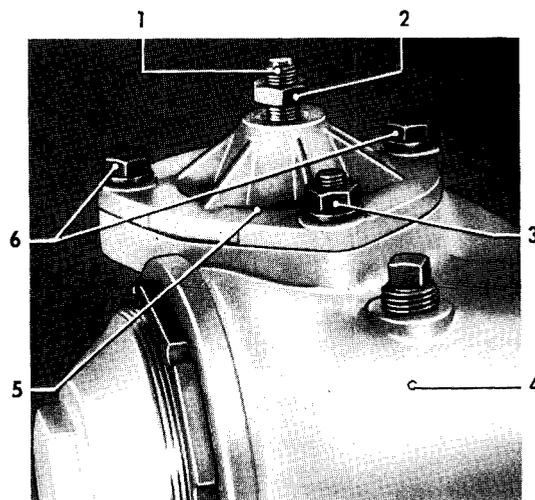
Lenkgehäusedeckel auf Lenkgehäuse aufgeschraubt
